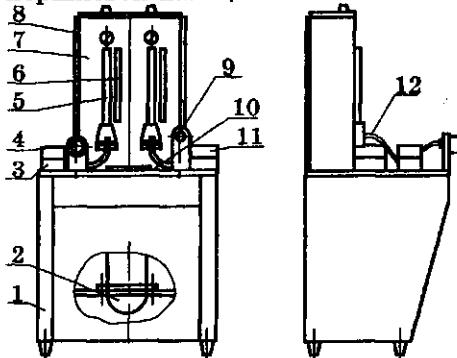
Схема стенда для сортировки шатунов на размерные группы: 1 — корпус; 2 — баллон; 3 и 11 — стабилизаторы давления; 4 и 9 — пневмопробки; 5 — трубка стеклянная; 6 — шкала; 7 — панель; 8 — щиток; 10 — плита; 12 — трубка полихлорвиниловая
